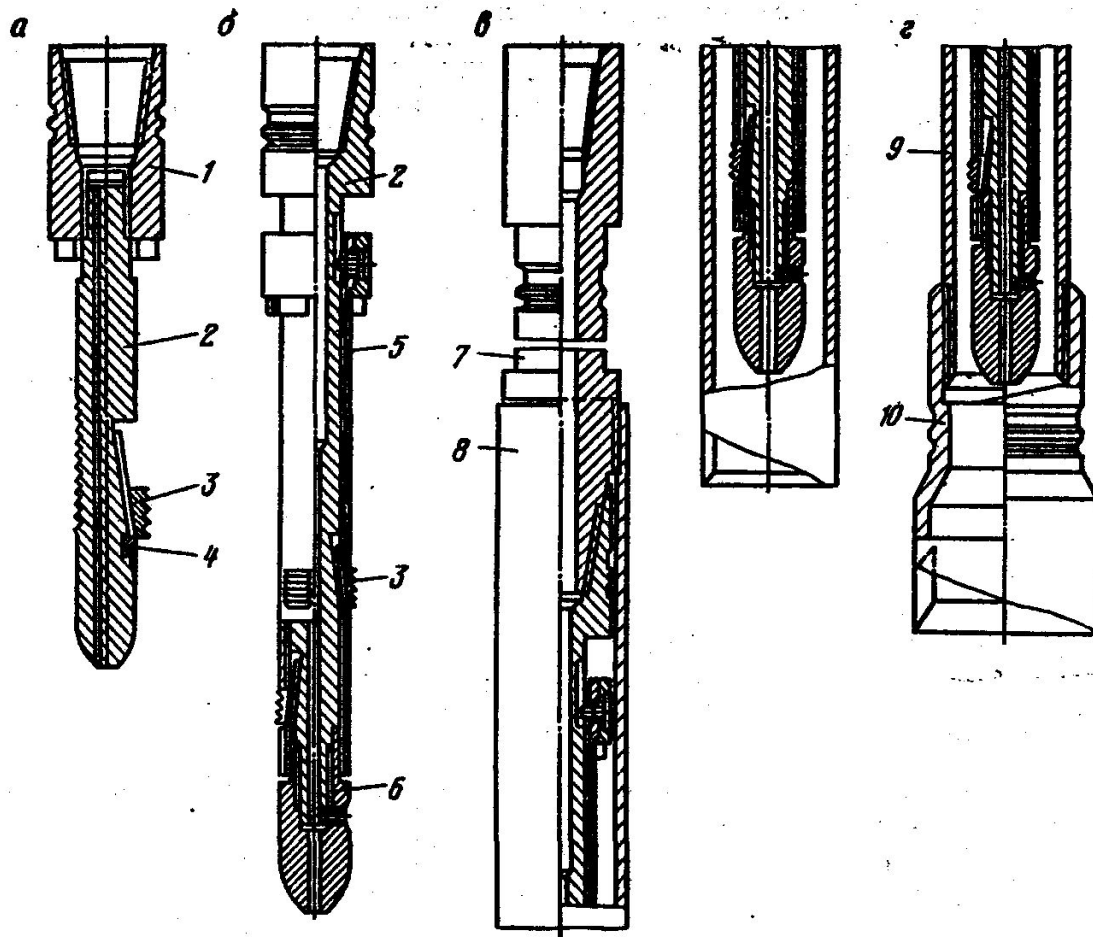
Труболовка внутренняя неосвобождающаяся ТВ:
